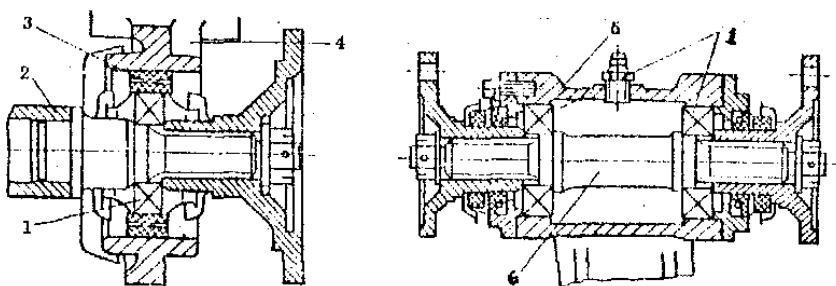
Проміжні опори: а – одноопорна; б – двохопорна; 1 – підшипники; 2 – карданний вал; 3 – гумова втулка; 4 – кронштейн; 5 – корпус; 6 – вал
